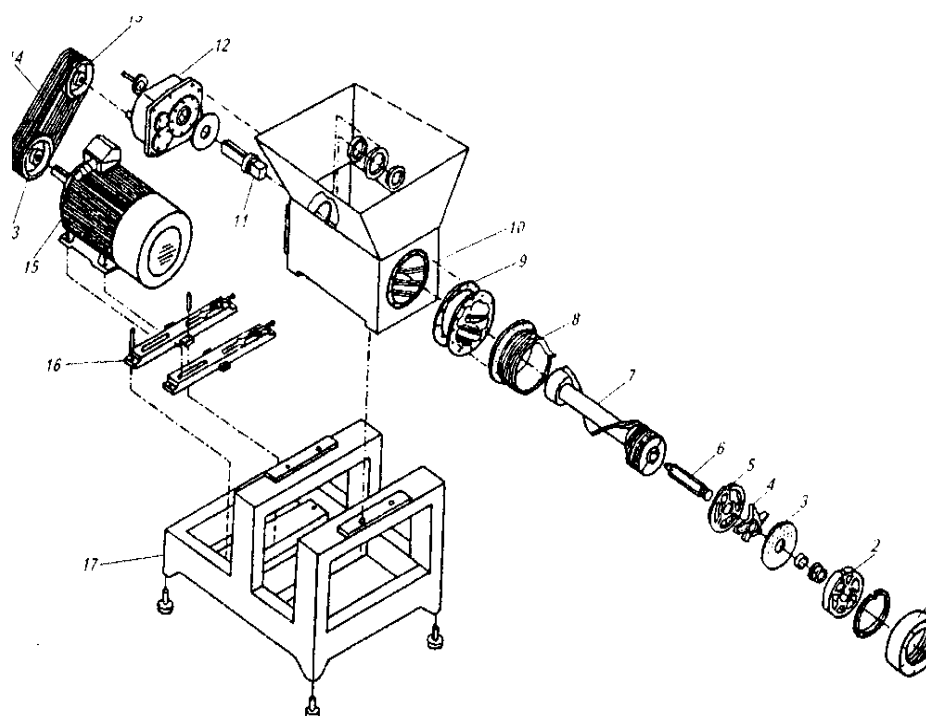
Волчок: 1 – затяжная шайба; 2 – опорный подшипник;
